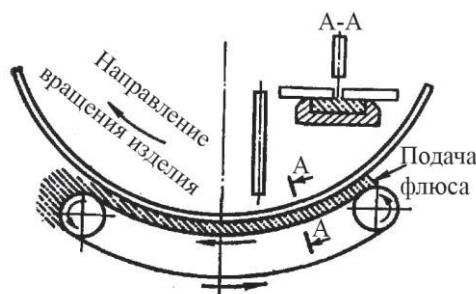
Флюсоременная подушка для сварки кольцевых швов
